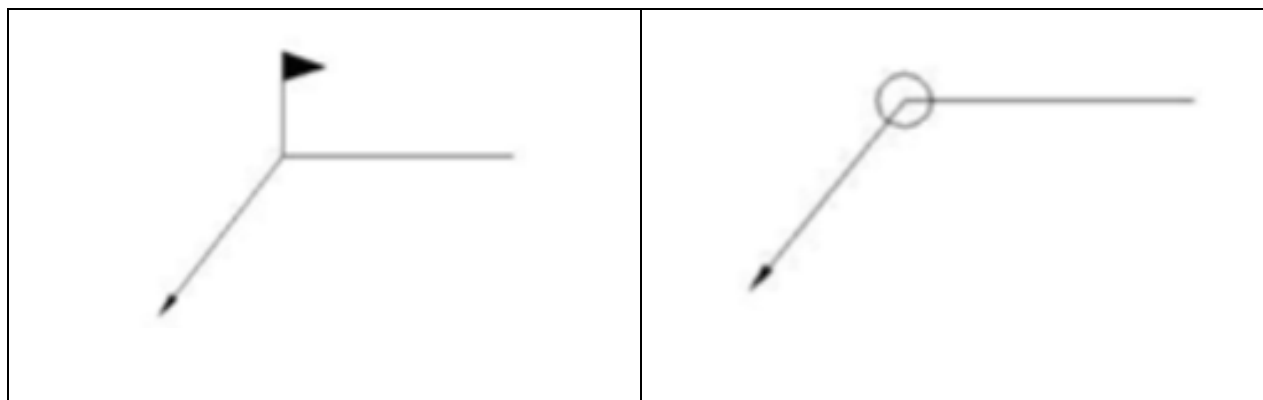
Indicador de soldadura en el campo u obra. Indicador de soldadura continua alrededor de la unión. Fuente: ISO 2553.
